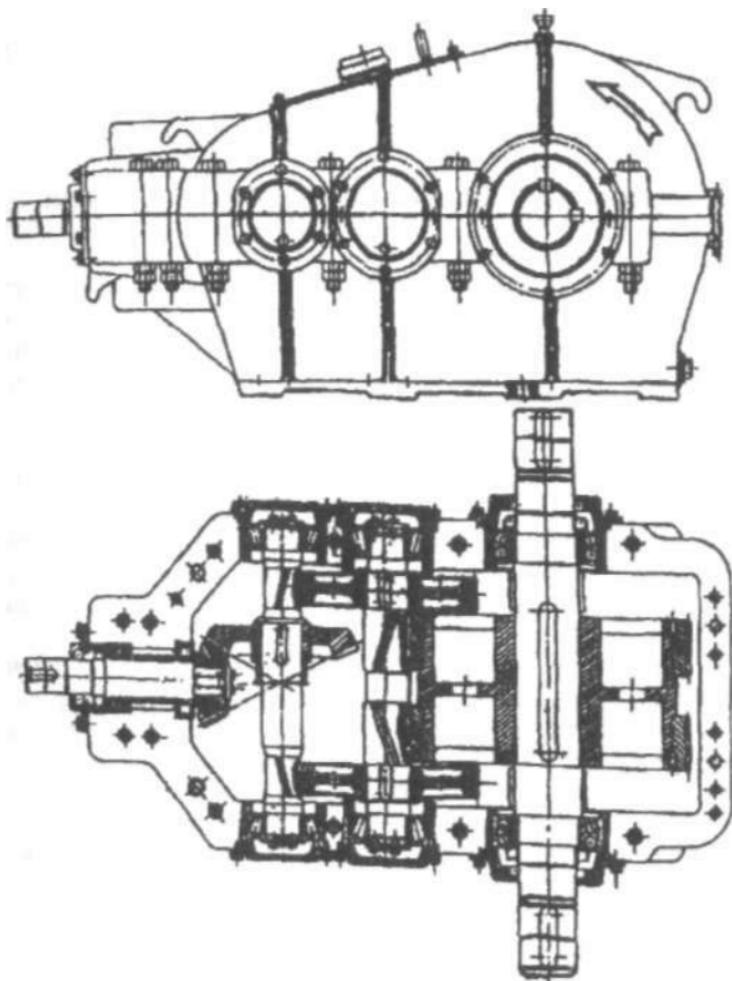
Трехступенчатый коническо - цилиндрический редуктор ЦЗНШ-315
